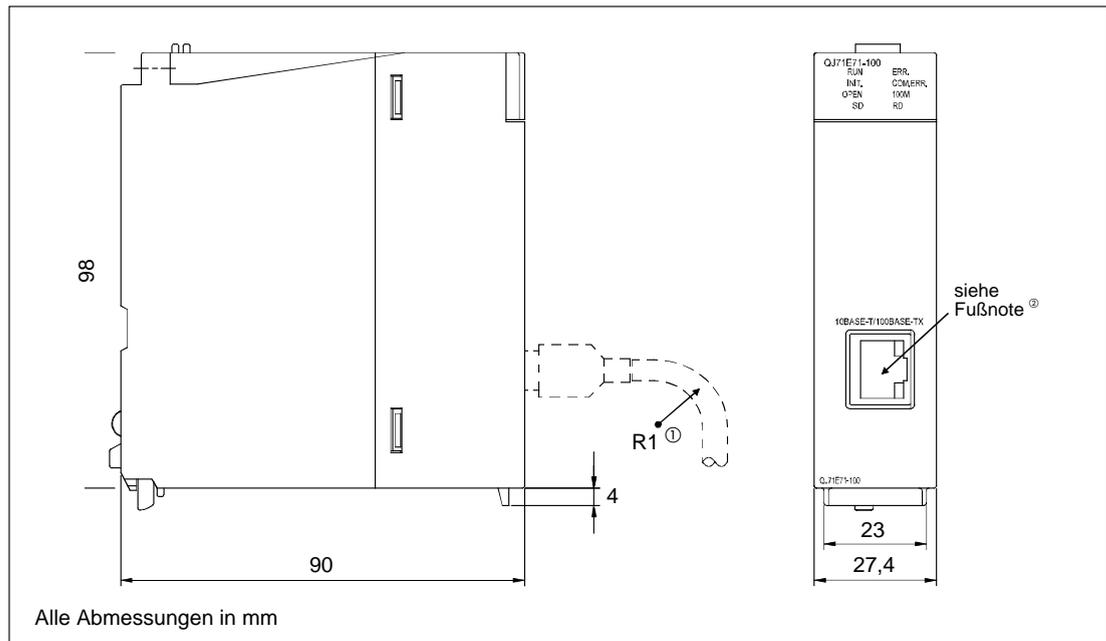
Gehäuseabmessungen des QJ71E71-100
